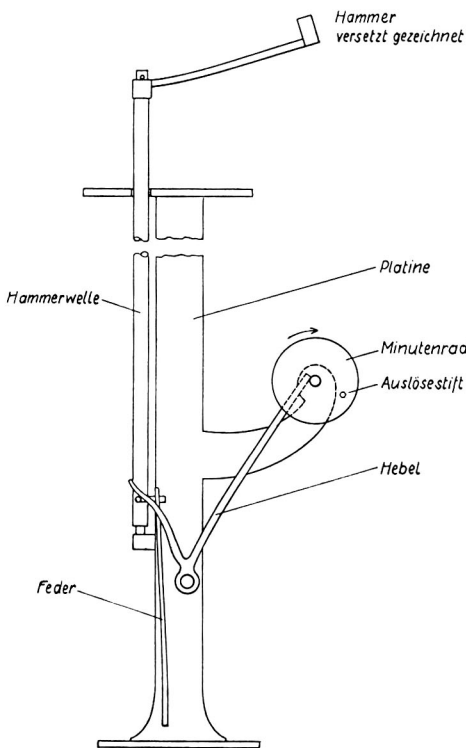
Halbstundenschlagwerk mit besonderem Hammer
